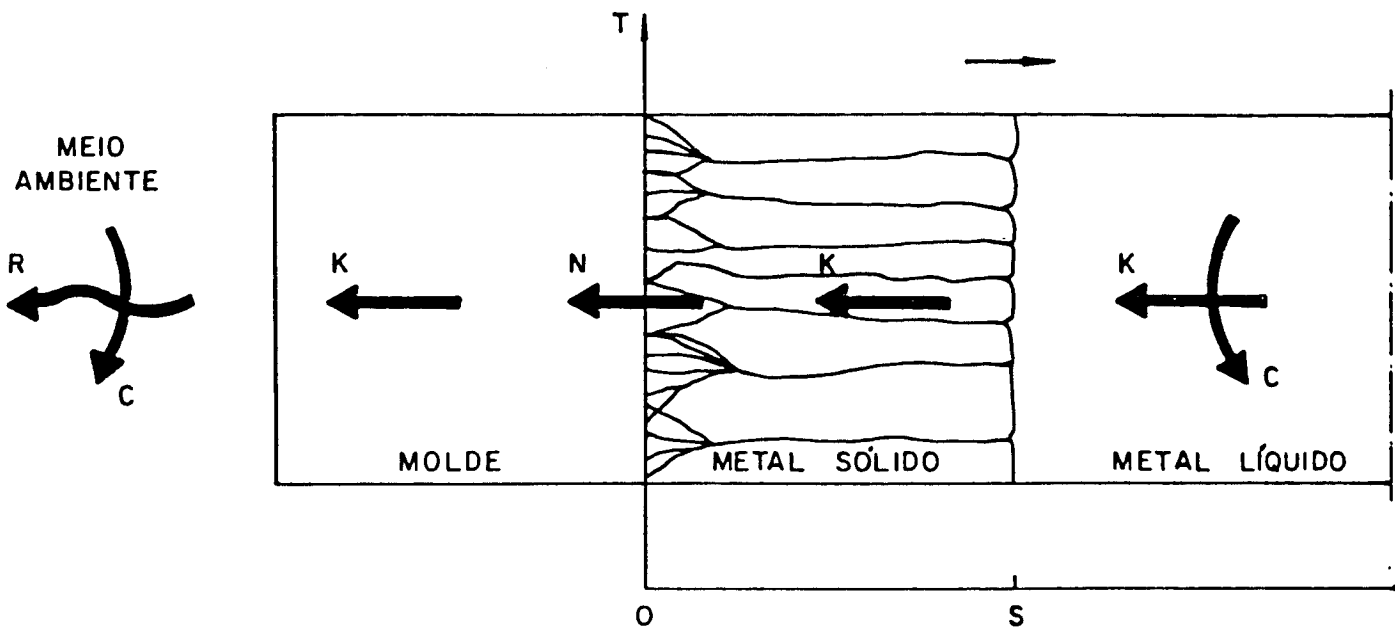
Sistema metal/molde em um instante qualquer do processo de solidificação.
